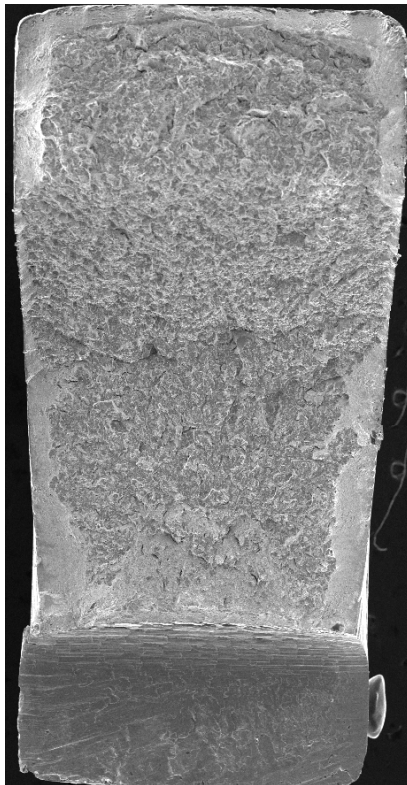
Superficie de fractura de la probeta B4-A-2.
